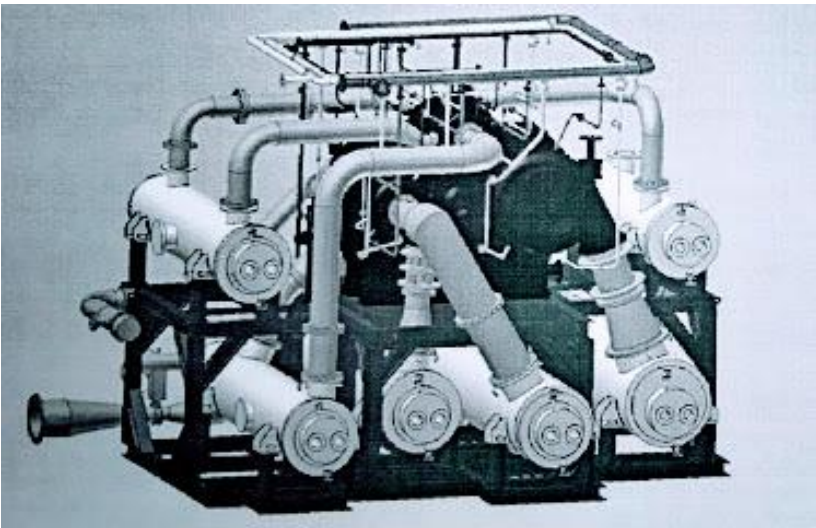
Компресор, оснащений проміжними охолоджувачами між окремими ступенями
